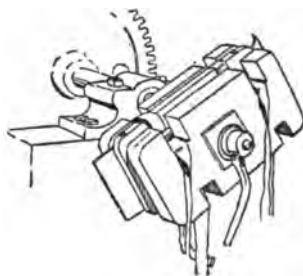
Exécution à la machine du bobinage d'un inducteur de rechange.
